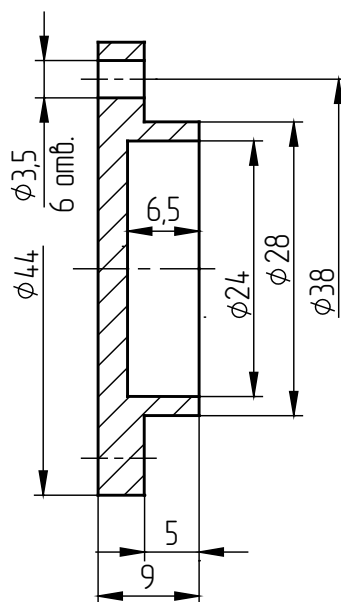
Учебный рабочий чертеж крышки, не учитывающий все особенности ее конструкции (с упрощениями)
